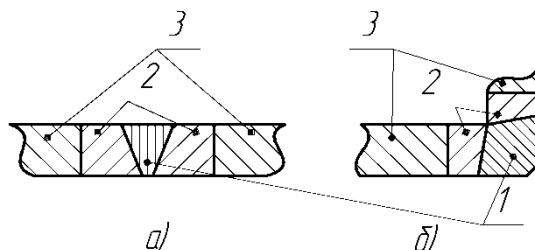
Форма поперечного сечения сварного шва:
